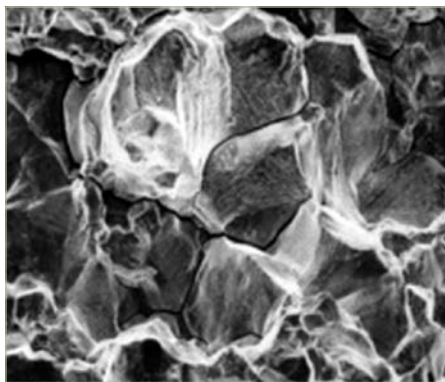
Superficie de Fractura de grieta generada por corrosión intergranular bajo esfuerzo.
